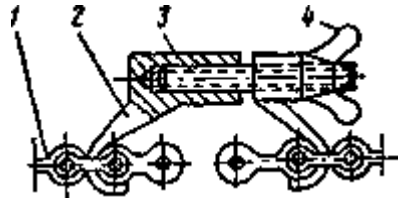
Стяжное приспособление для втулочно – роликовых цепей.
